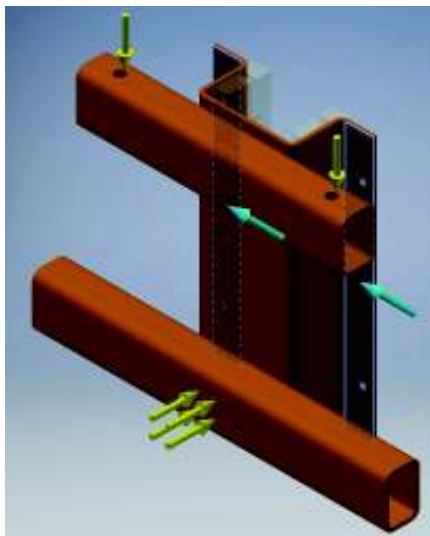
Cargas y restricciones sobre el carro elevador.
